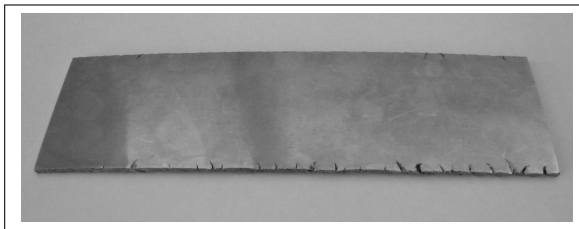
Walzgut mit Kantenrissen nach 31 Stichen
